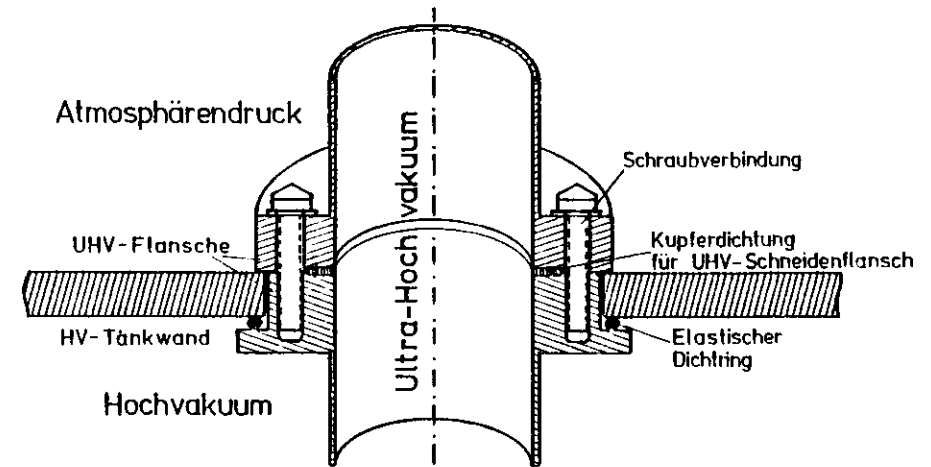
Schnitt durch die Flanschverbindung mit Doppeldichtung
